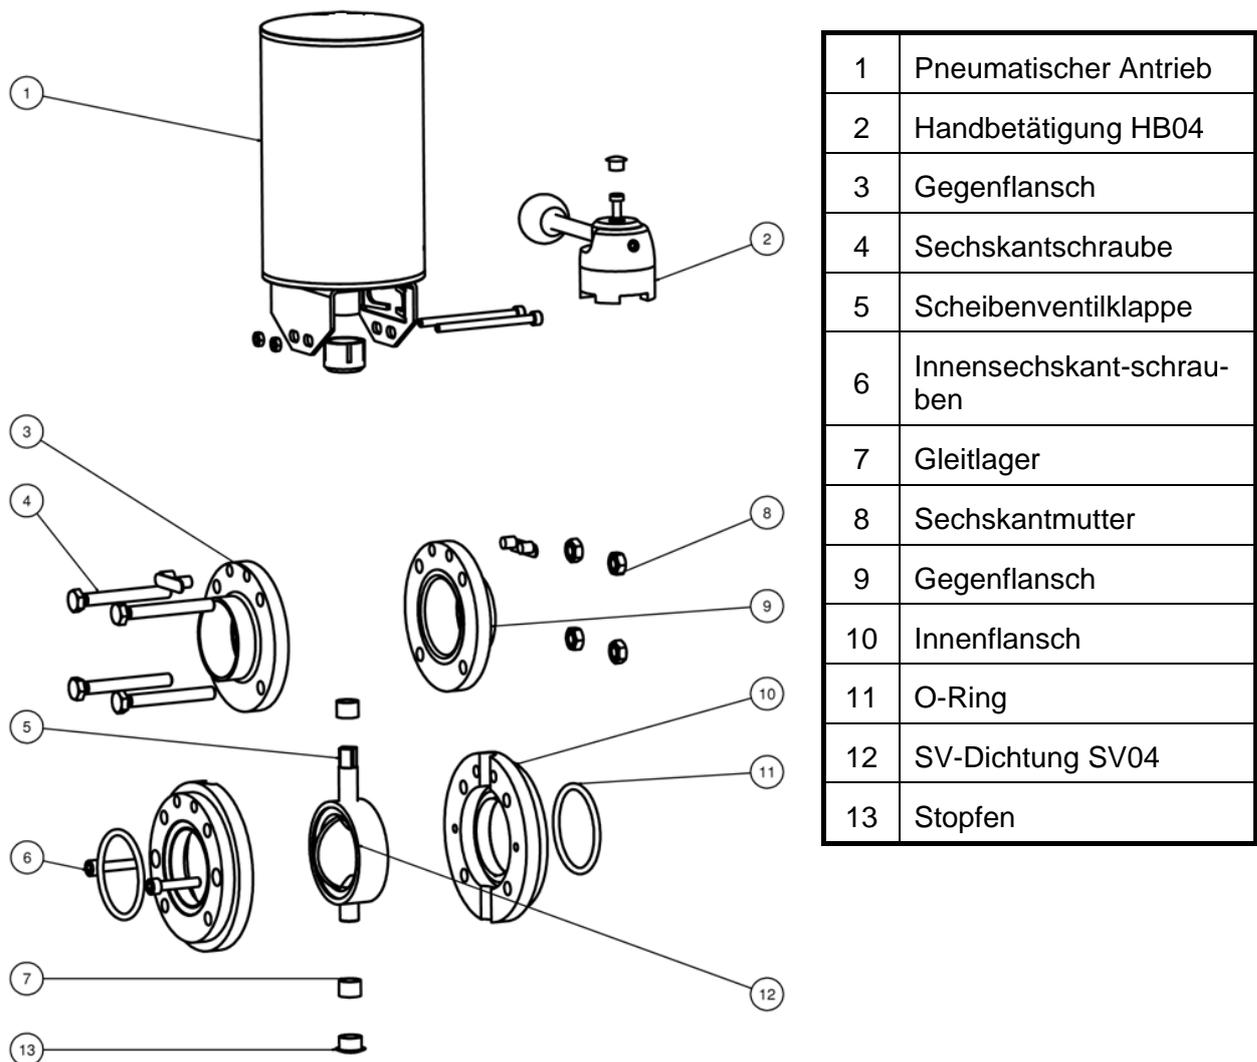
Demontage Scheibenventil SV04 ZF mit HB04 PAMS
